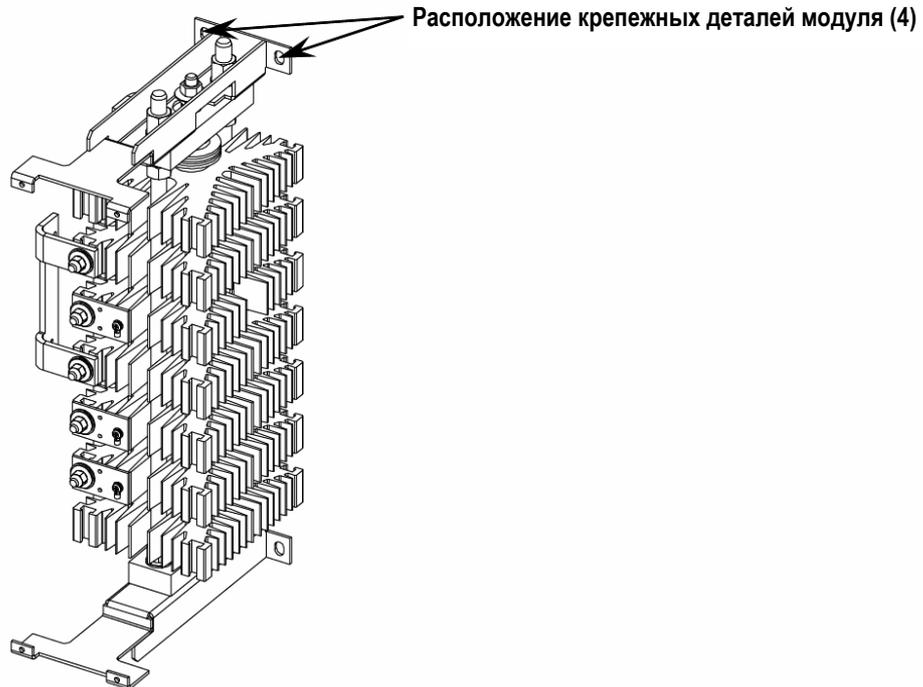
Сборка силового модуля (одна фаза) со снятыми платами формирователей и корпусом • 5500 / 6900 В, 180 А / 360 А
